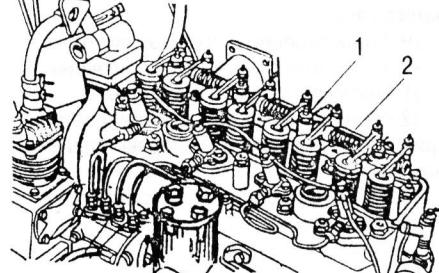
Снятие механизма коромысел: 1 – гайки крепления механизма коромысел; 2 – механизм коромысел в сборе
